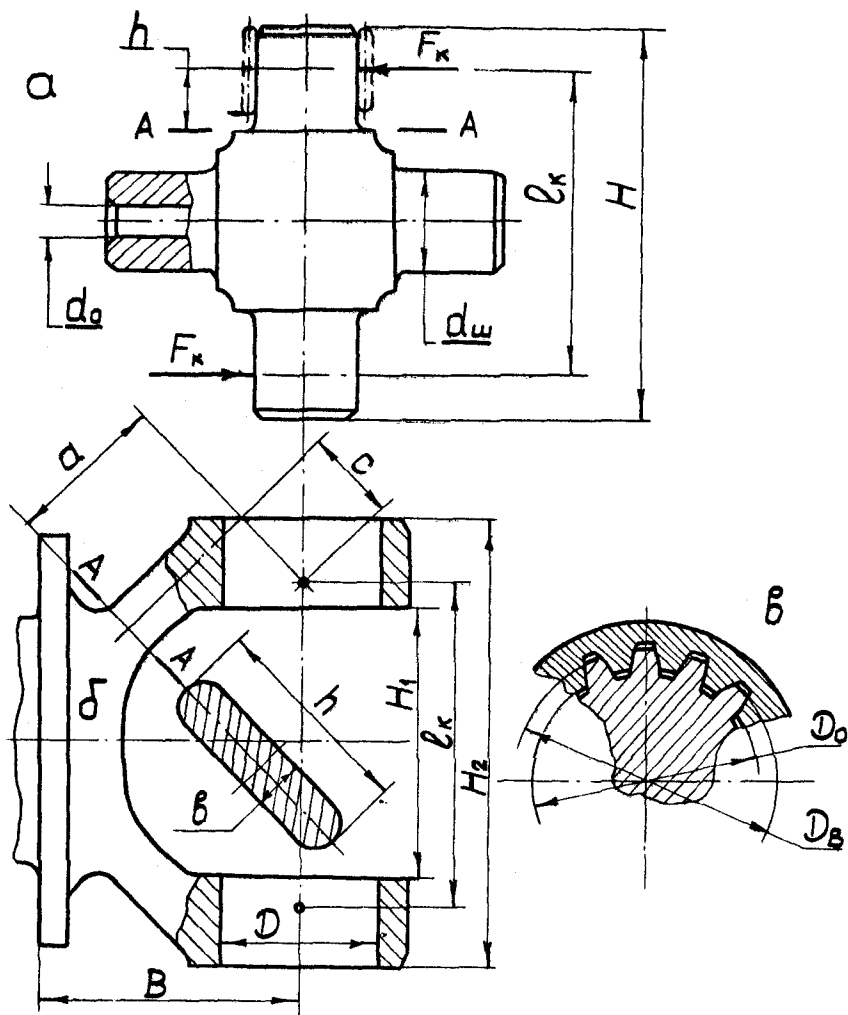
Элементы шарнира и шлицевого соединения скользящей вилки: а - крестовина шарнира; б - вилка шарнира; в - сечение шлицевого соединения скользящей вилки
